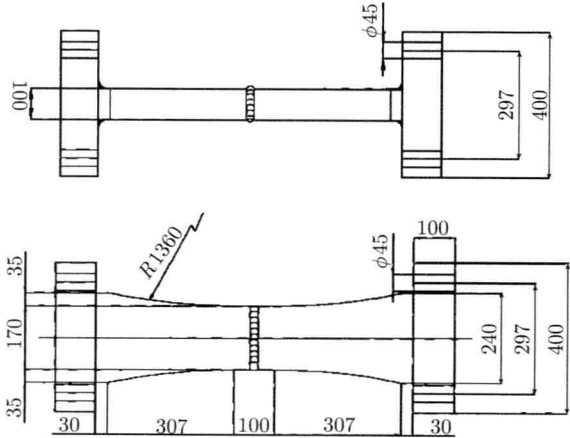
厚板横向对接焊接接头试件 (单位: mm)
